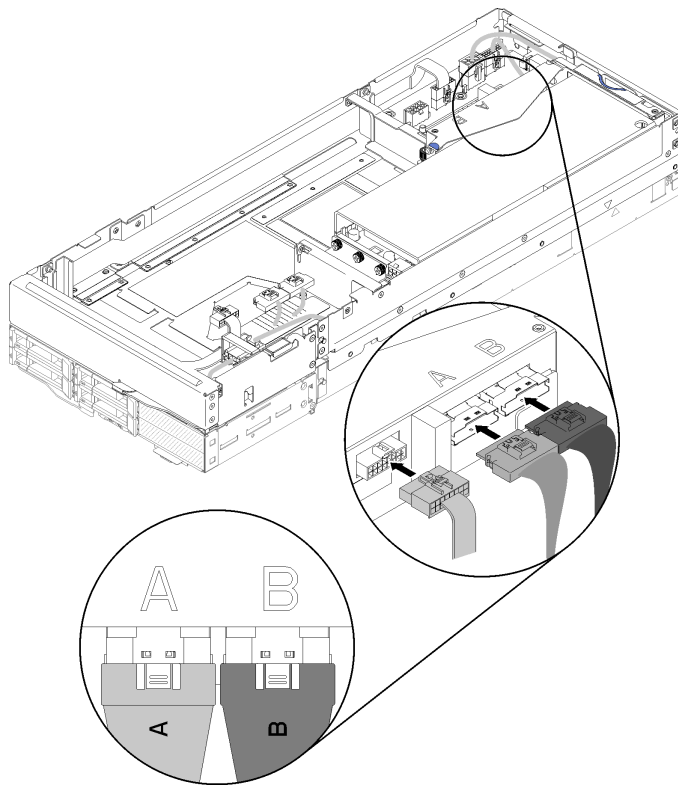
Connexion du câble PCIe#1-A, PCIe#2-B et du câble à usage divers de carte mezzanine à l'assemblage de cartes mezzanines arrière
